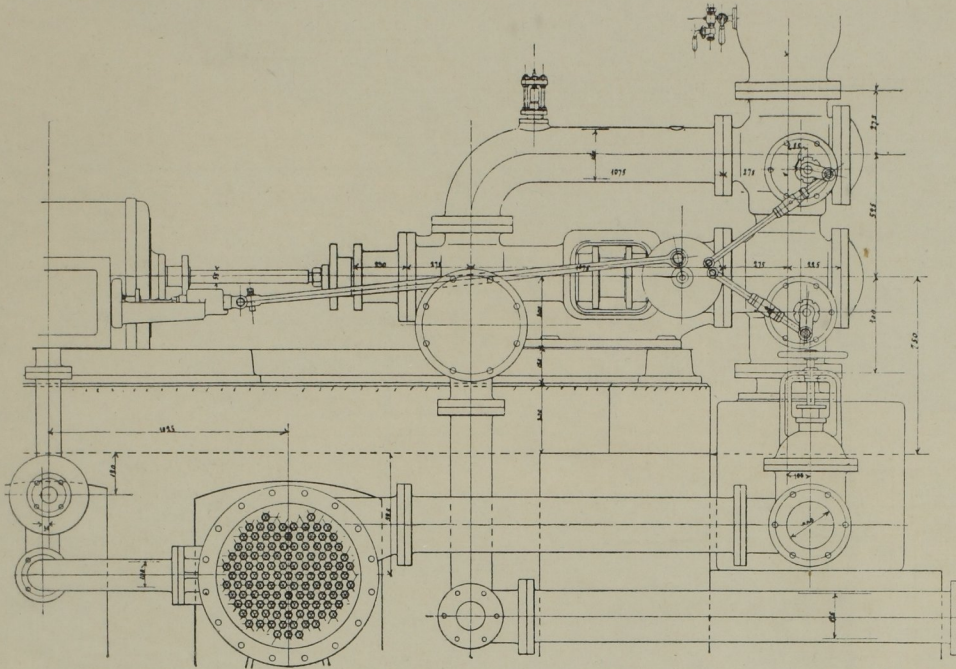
Seitenansicht der Pumpe. Masst. 1:30.
